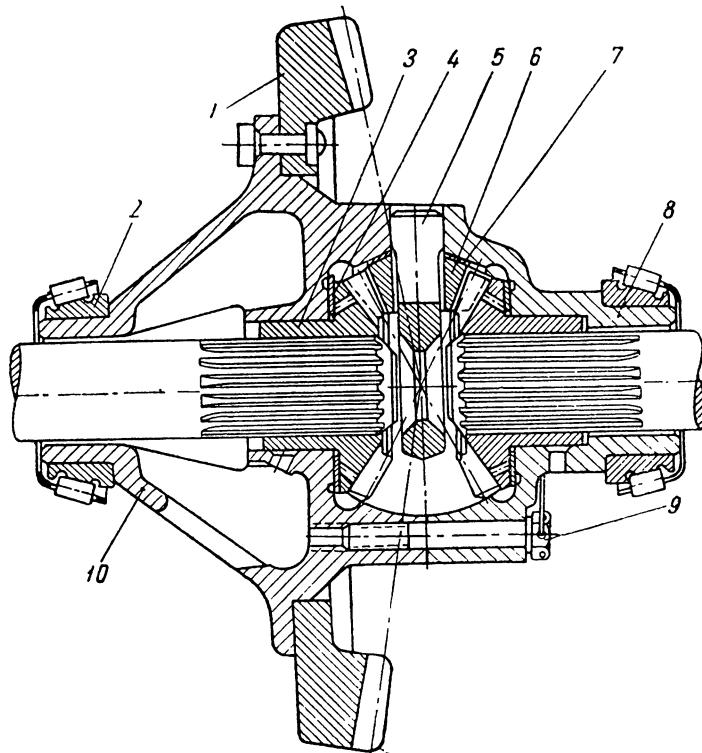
Сборка узла ведомой шестерни главной передачи и коробки сателлитов
